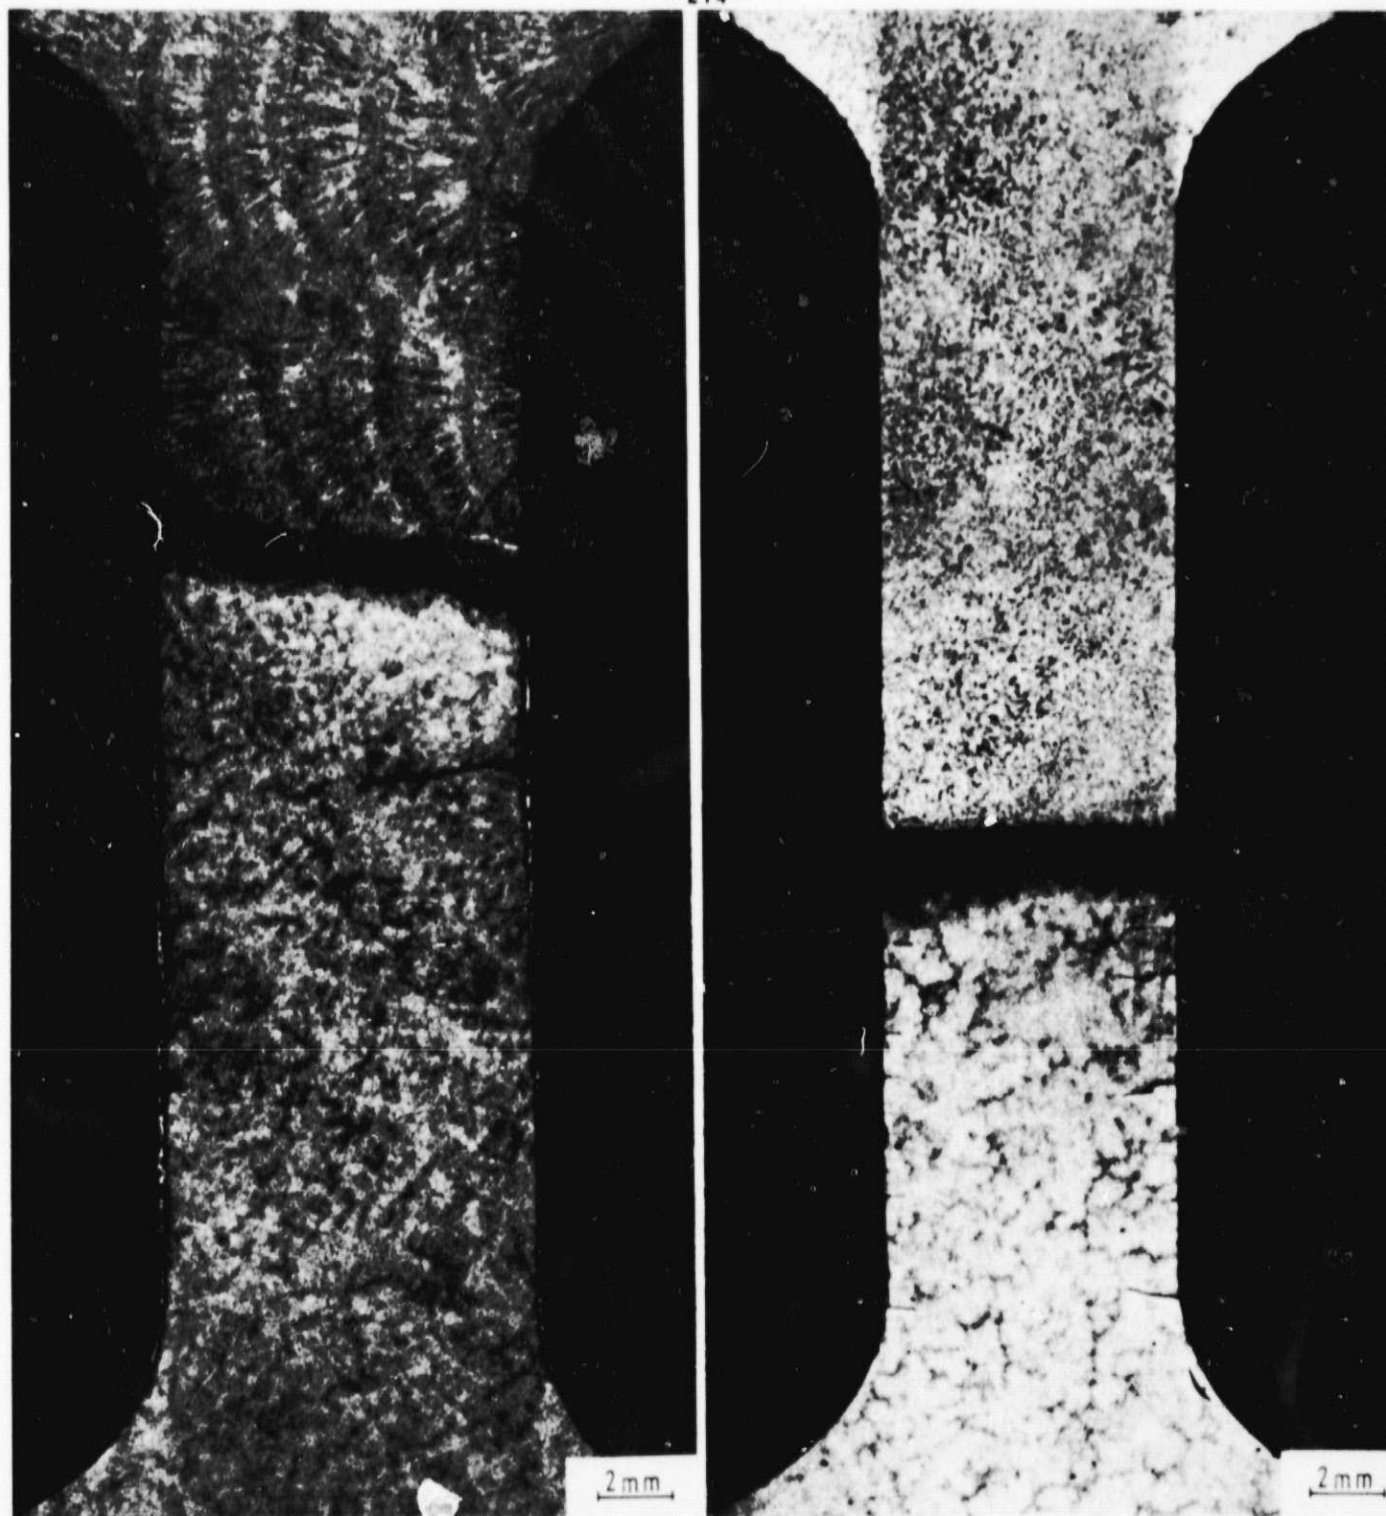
Anrißbildung bei den Querschweißproben der Schweiß-
